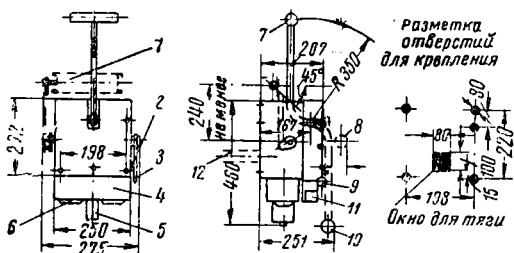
Привод типа ПРА-10; 1—стальное основание; 2—вал; 3—механизм свободного расцепления; 4—сигнальный рычаг; 5—сигнальные контакты; 6—включающий рычаг; 7—вилка; 8—муфта; 9—указатель положения; 10—медальон; 11—отключающие электромагниты; 12—переключатель числа витков; 13—зажимы; 14—реле минимального напряжения; 15—болт для заземления
